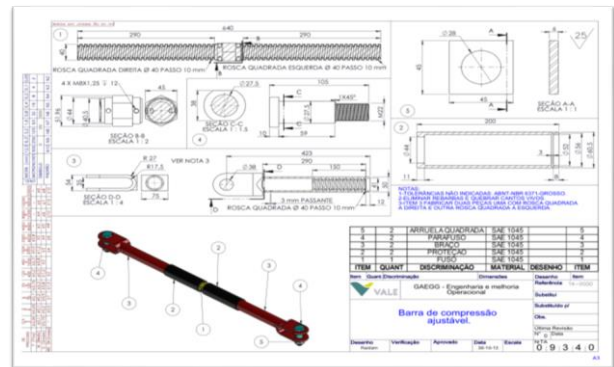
Desenho Técnico da Barra de Compressão Ajustável.
